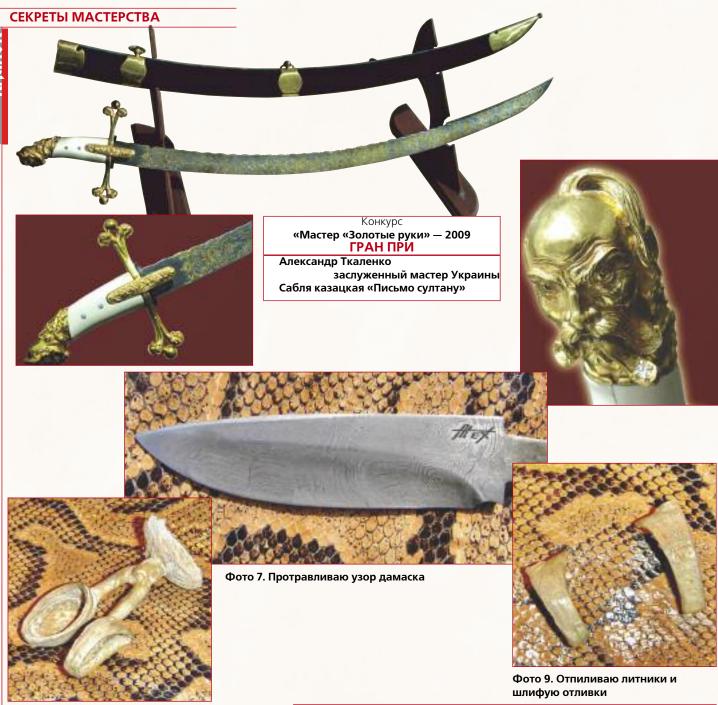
Делаю отливки из серебра для полугарды и навершия рукояти
